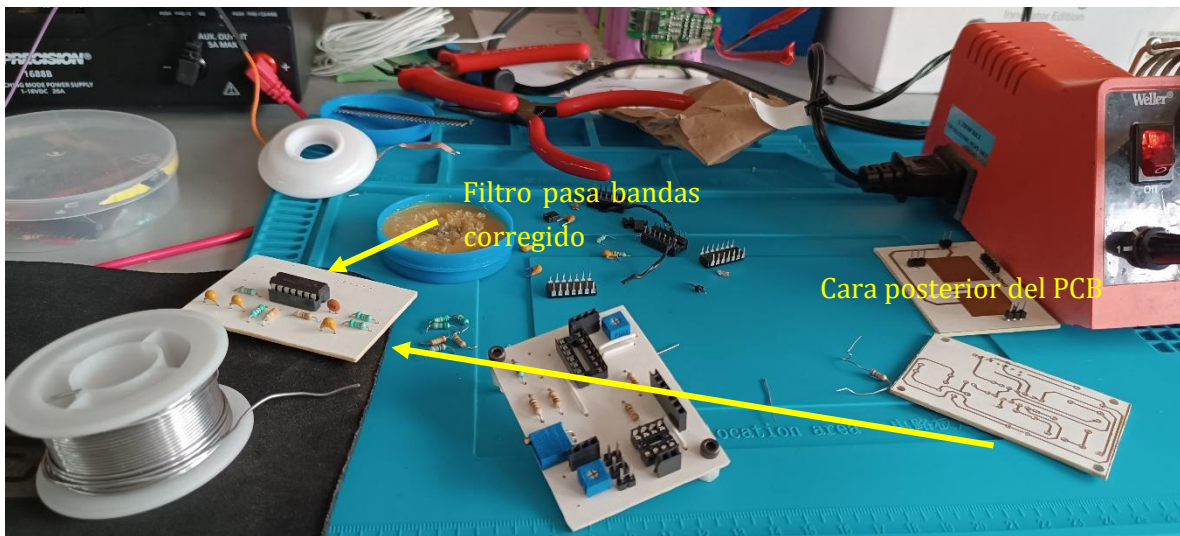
40: Proceso de fabricación de primera versión del filtro pasa bandas, utilizando componentes tradicionales.
